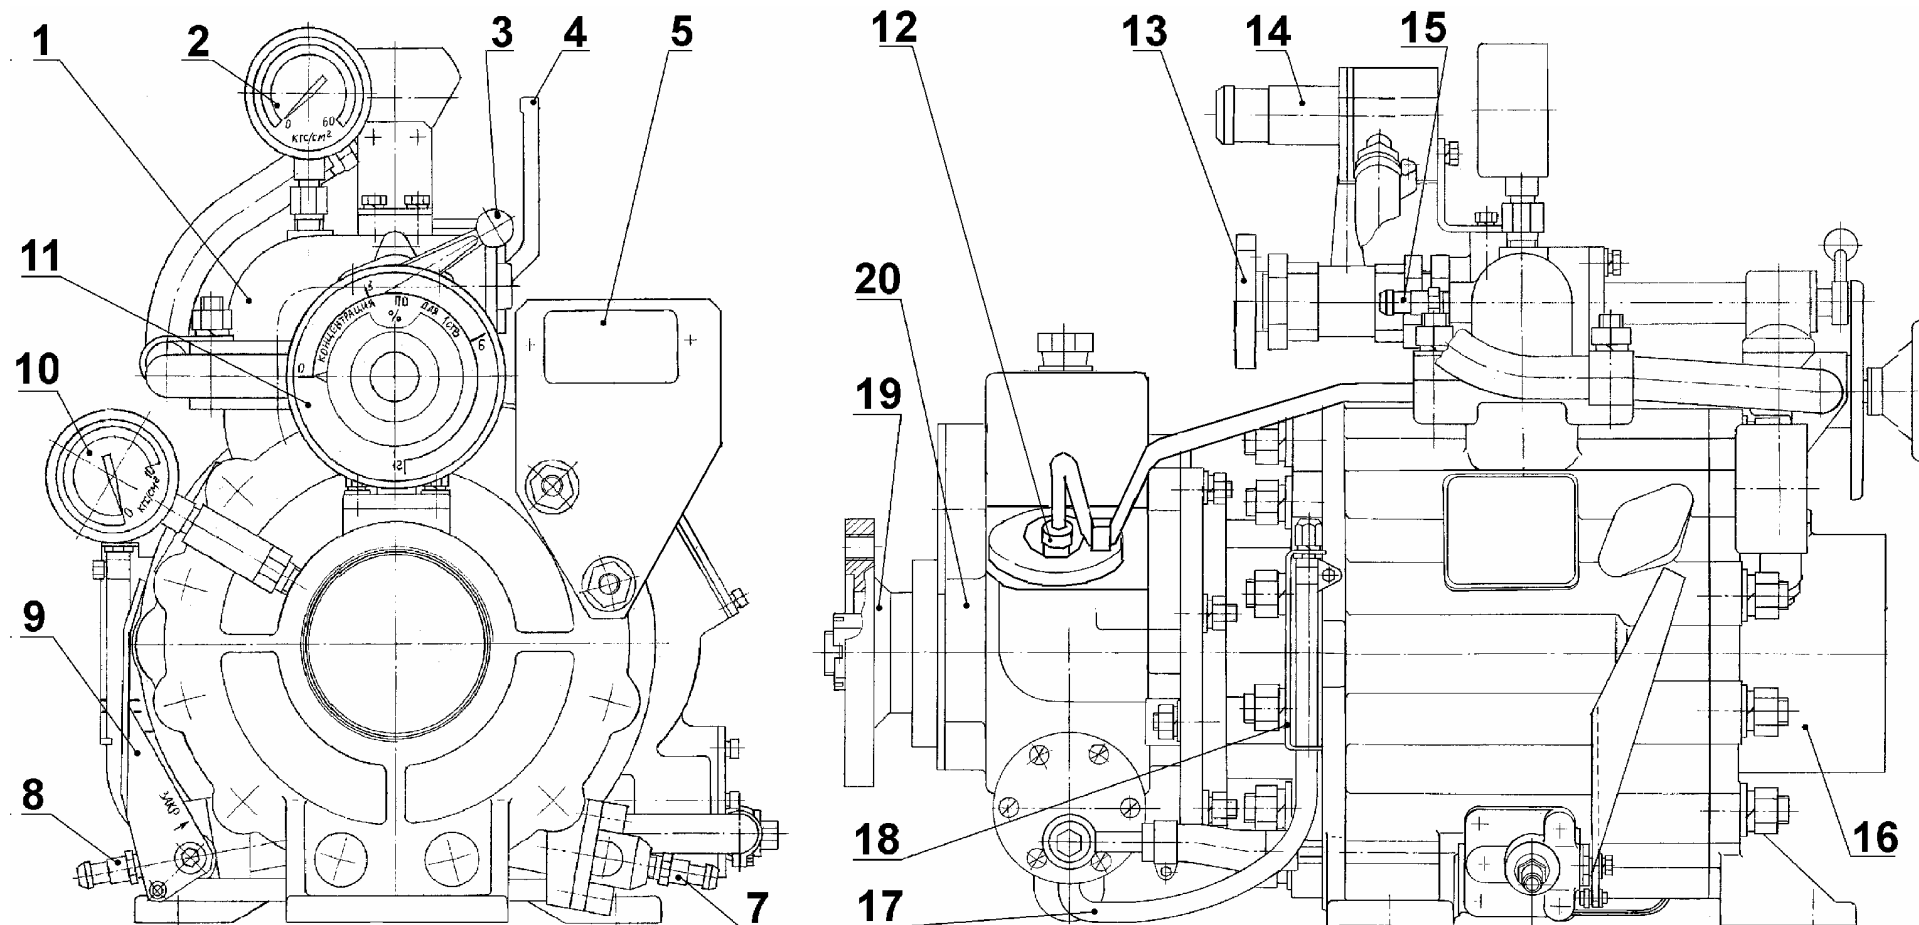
Общий вид насоса НЦПВ-4/400РТ: 1 - напорный коллектор; 2 - манометр на выходе (60 кгс/см²); 3 – рукоятка крана включения эжектора; 4 – кран напорный; 5 – блок индикации тахометра; 7, 8 - сливные краны; 9 - рукоятка механизма управления сливными кранами; 10 - манометр на входе (10 кгс/см²); 11 - пеносмеситель; 12 – датчик тахометра; 13 - фланец напорного патрубка; 14 - узел подвода пенообразователя; 15 - штуцер перепускной магистрали; 16 - насос центробежный; 17 - трубка маслоуказателя; 18 - кронштейн; 19 - полумуфта; 20 - редуктор.
